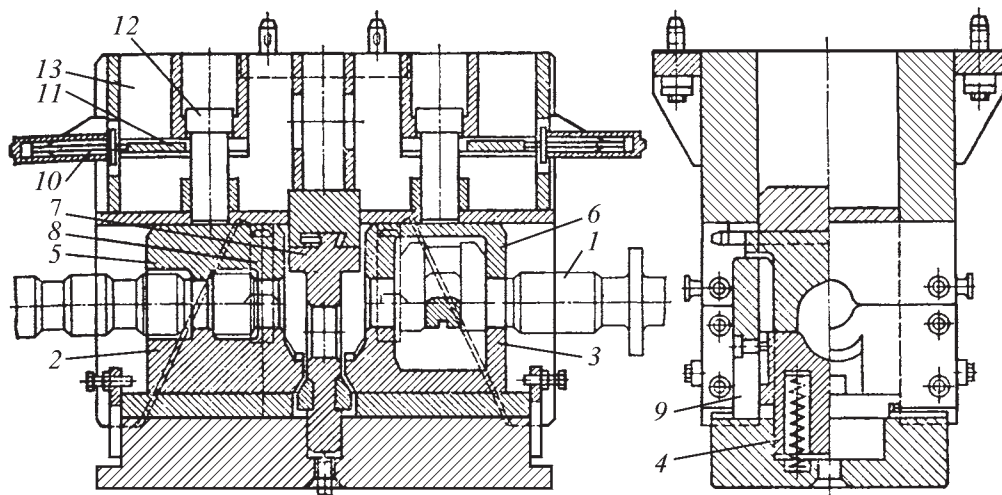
Схема штампа-установки клинового типа (продольный разрез) для штамповки методом гибки с высадкой (конструкция ВПТИ)
